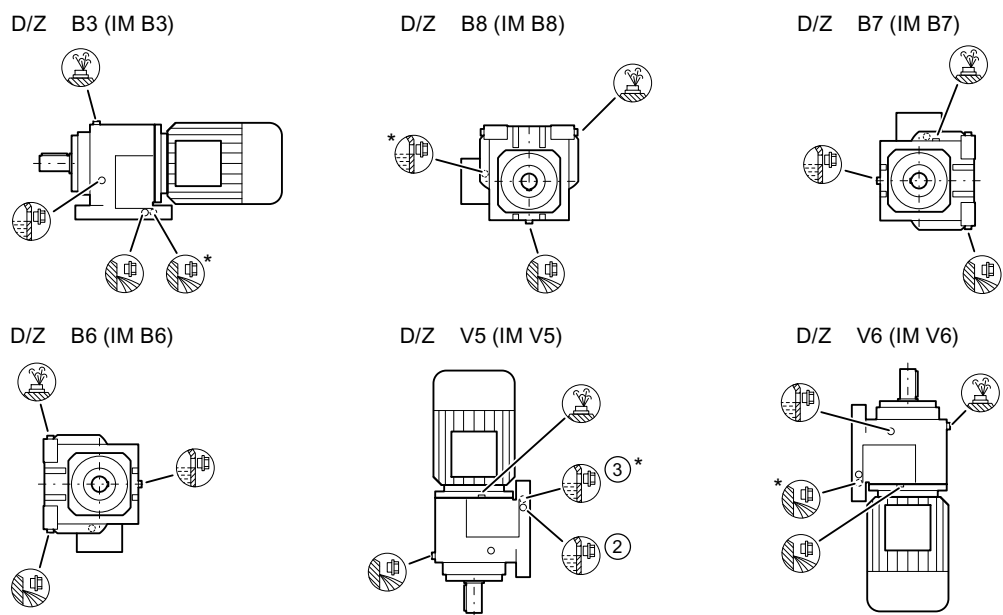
Konstrukcje dla E. Wielkości 38 - 148
